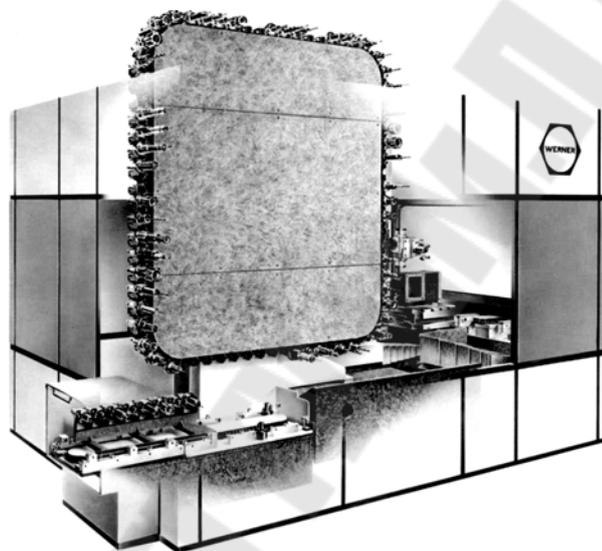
Обрабатывающие центры с цепным магазином и устройством скоростной смены инструментов (QTC)
